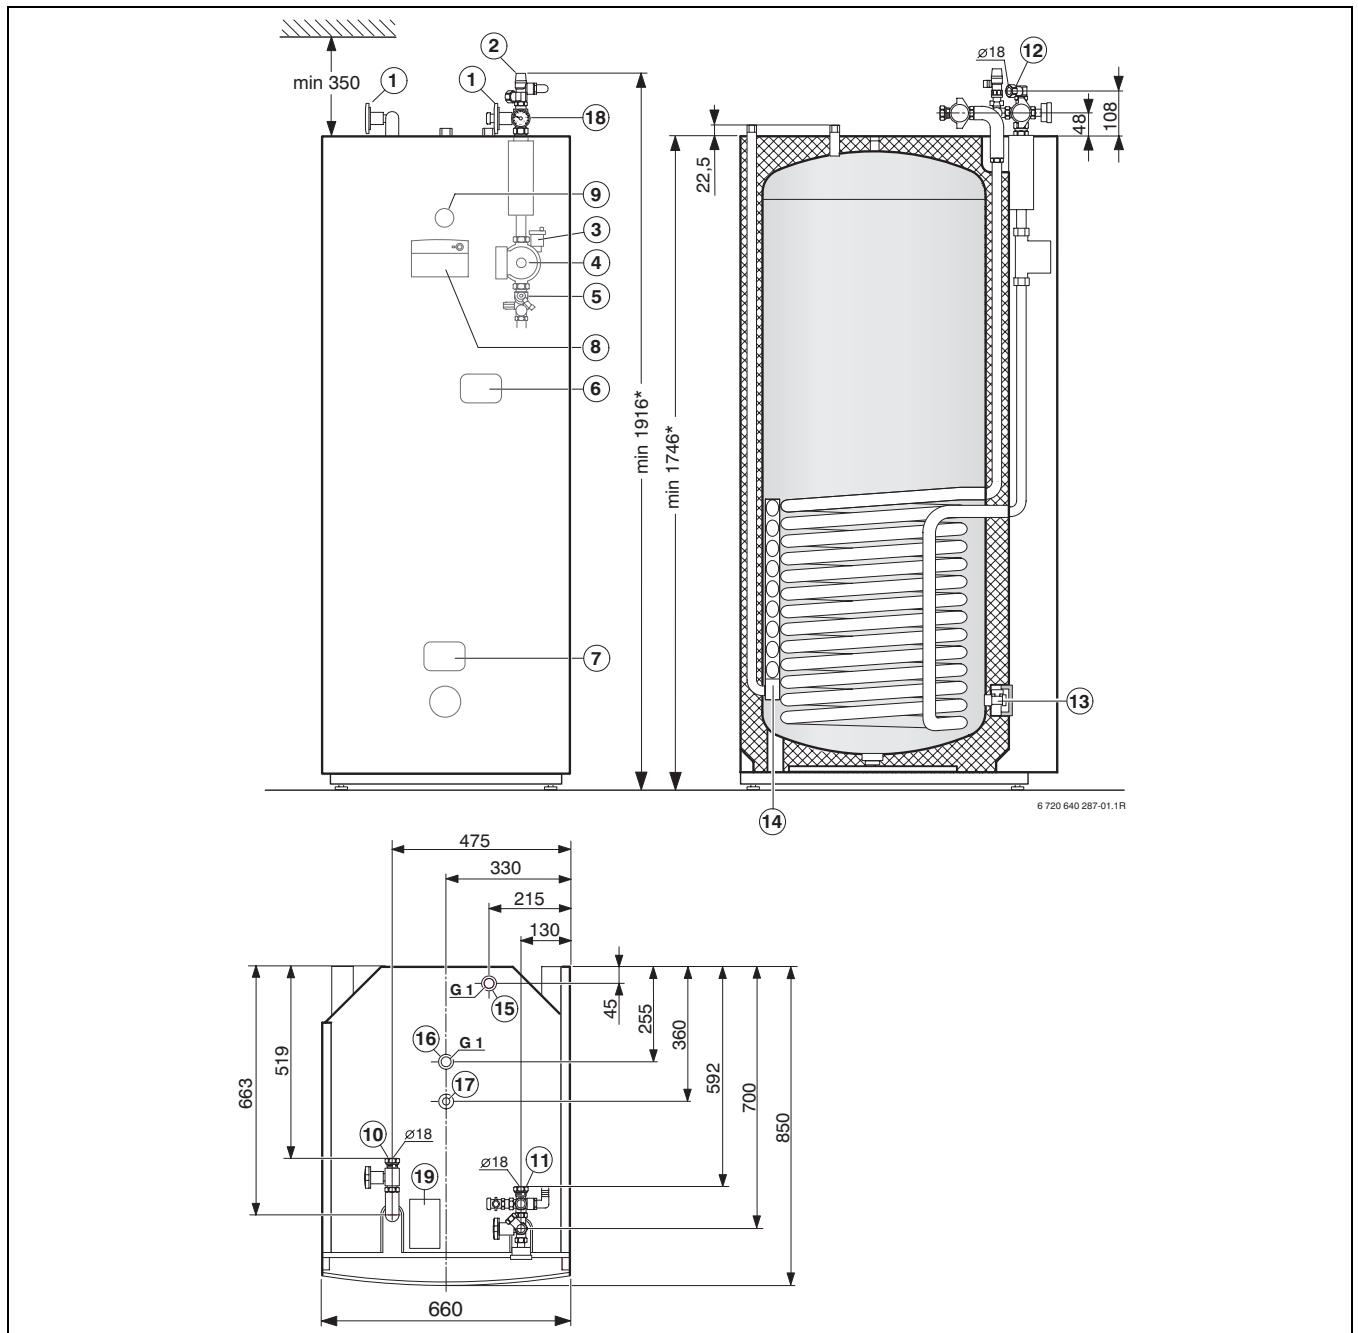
Dimensões de construção e de ligação SP 400 SHU
